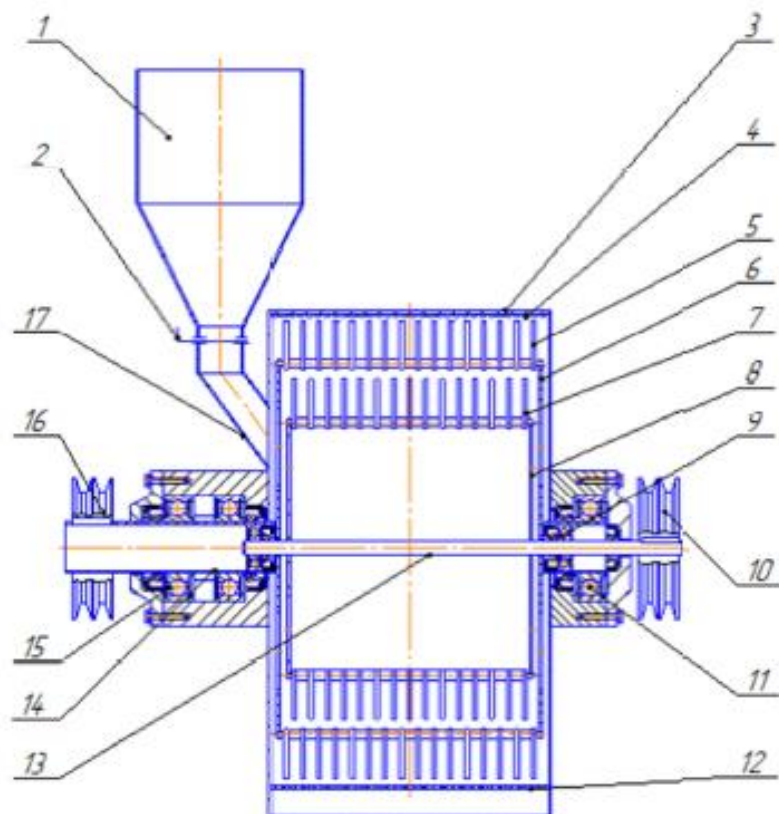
Комбінована дробильна камера: 1 – бункер завантажувач; 2 – дозувальна заслінка; 3 – камера подрібнення комбінована; 4 – дека; 5 – молоток; 6 – зовнішній дробильний барабан; 7 – ніж; 8 – ножовий барабан; 9 – внутрішній підшипник; 10 – шків; 11 – зовнішній підшипник; 12 – решето; 13 – вал внутрішній; 14 – вал зовнішній; 15 – підшипник зовнішній; 16 – шків; 17 – подавальна труба.
